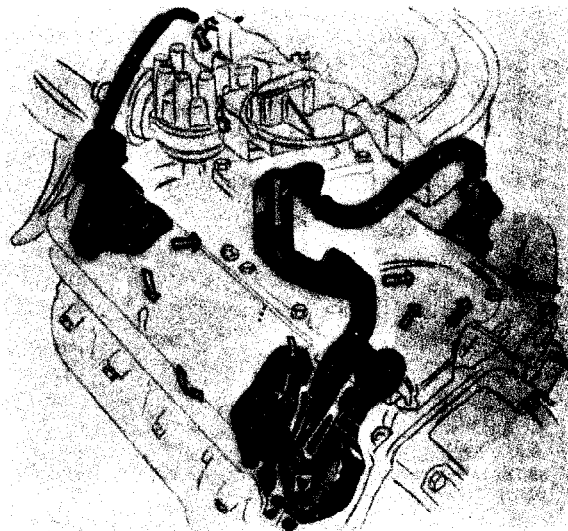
Sistema cerrado de ventilación del cárter en un motor de 8 cilindros en V (Ford Division of Ford Motors Company).
